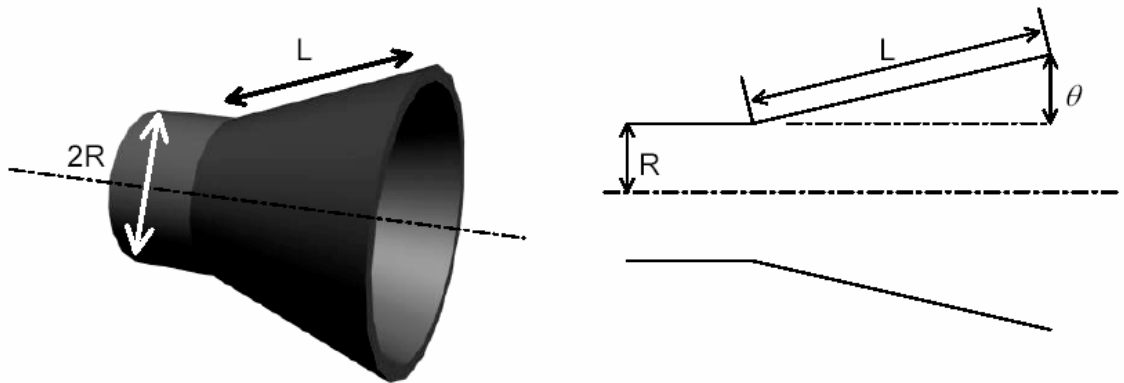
Difusor cônico em desenho tridimensional e corte radial
